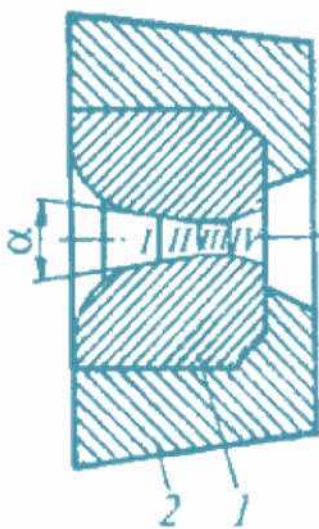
Загальний вигляд волоки: 1-волока; 2-обойма.
